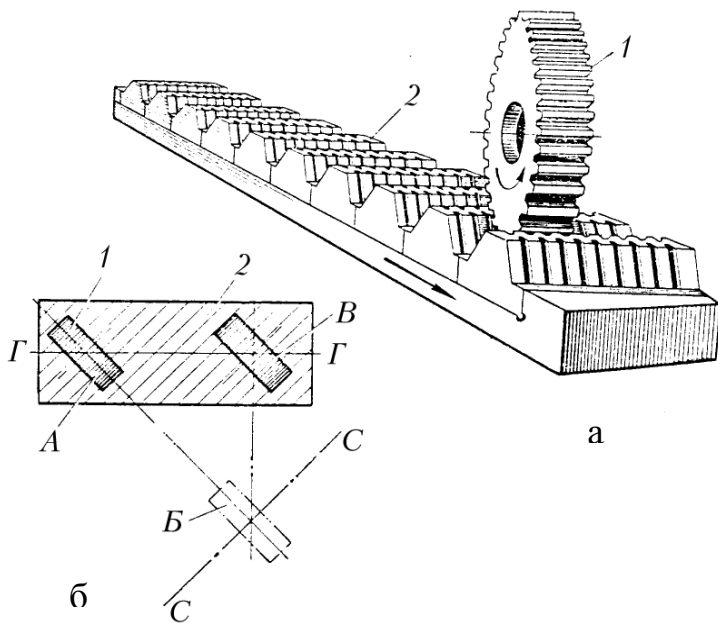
Шевінгування шевером-рейкою: а – шевер-рейка; б – схема ковзання шевера-рейки по зубах шестерні.
